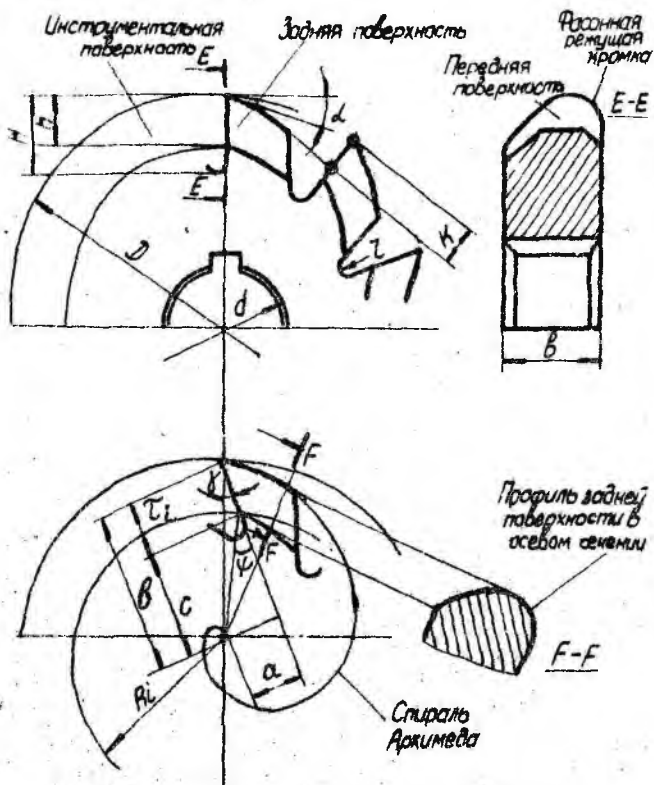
Конструктивные и геометрические параметры фасонной фрезы
